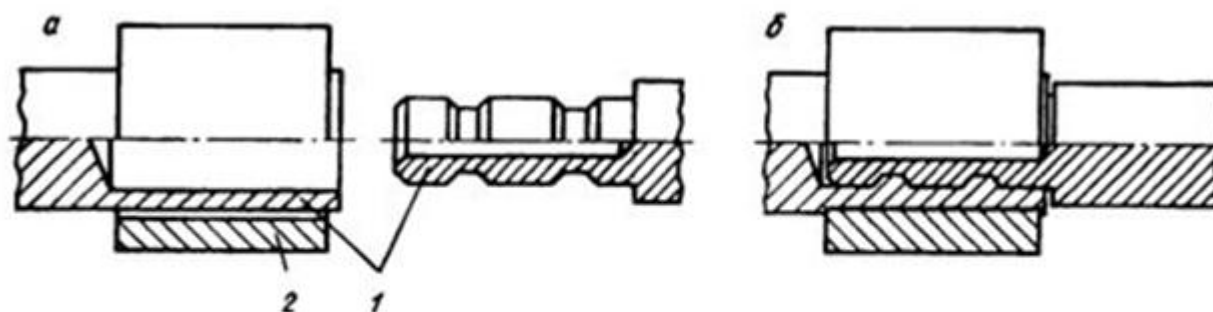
Соединение трубчатых деталей (1) с помощью муфты (2) из металла с памятью формы: а – до сборки; б – после нагрева [6]
